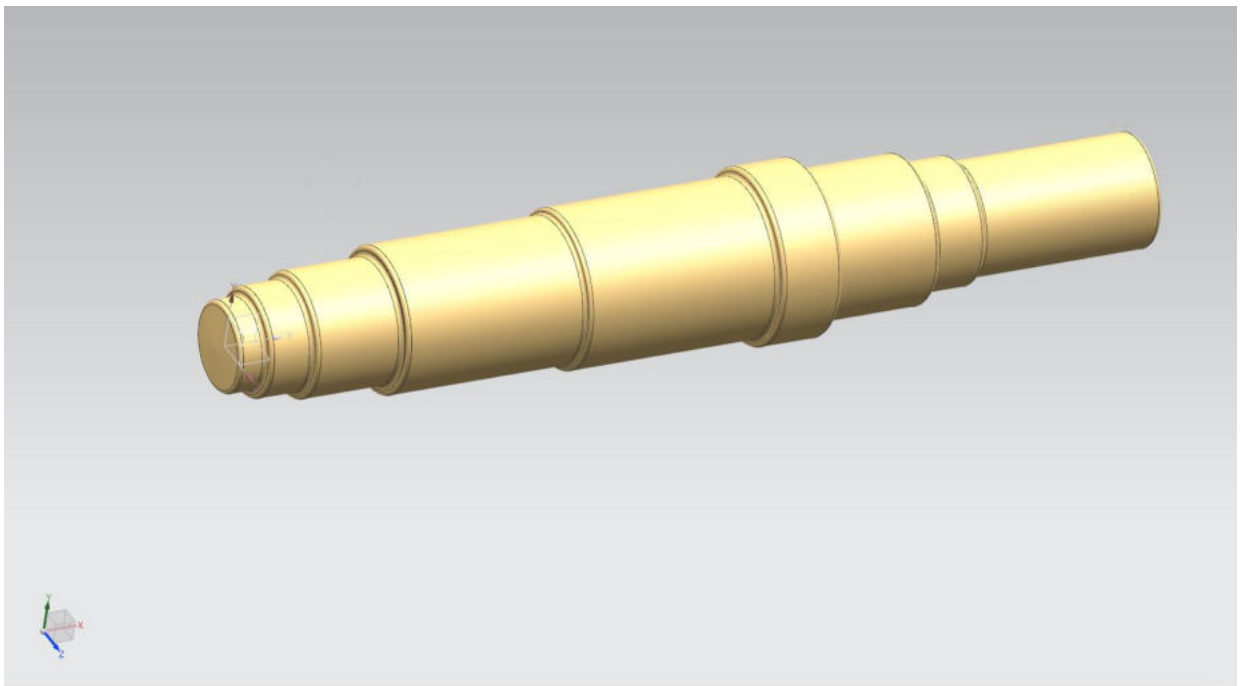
Ескіз 3D-моделі заготовки методом КГШП
